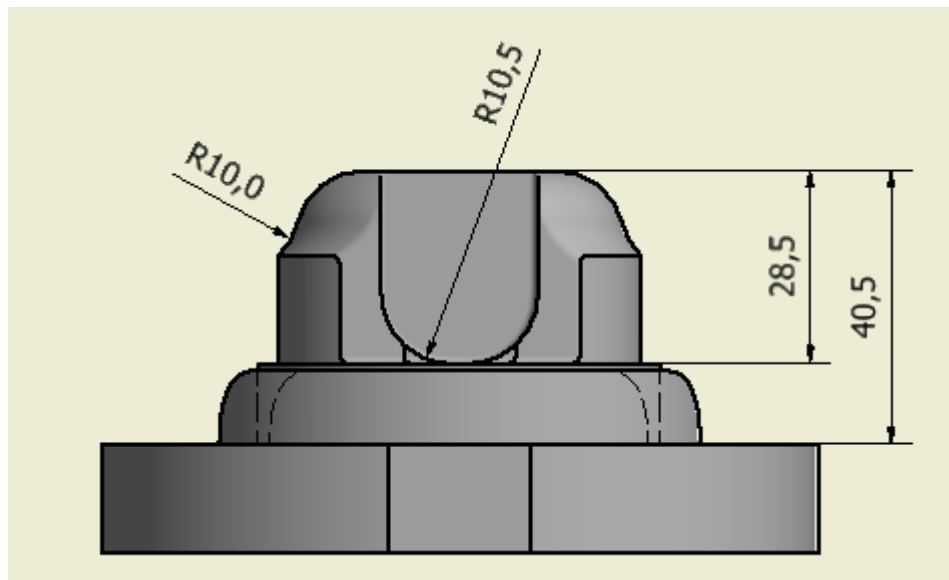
Vista frontal del sistema de fundición interna del pistón.
